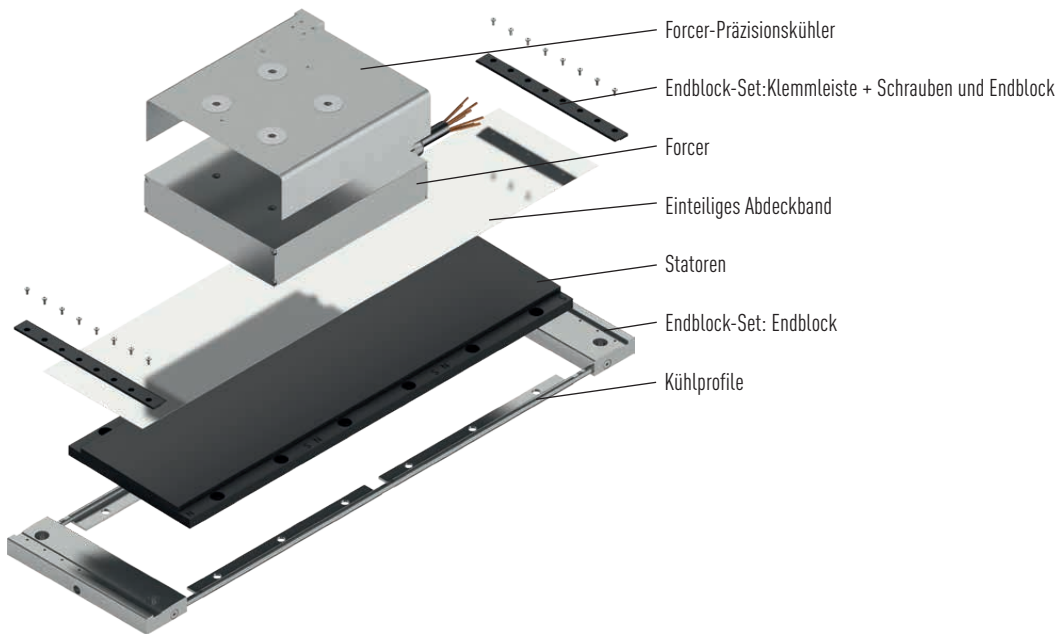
Explosion: LMFP41-Linearmotor mit Präzisionskühlung für Forcer und Stator und einteiliger Stator-Abdeckung
